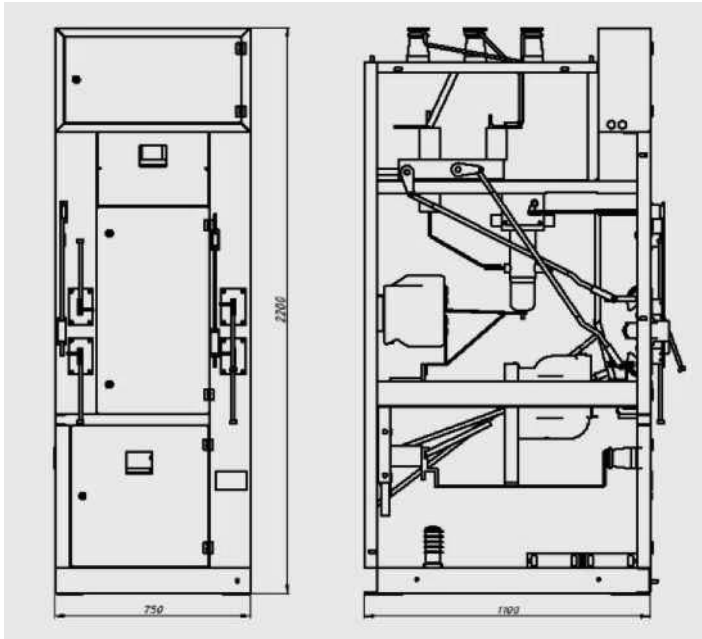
Внешний вид и габаритные размеры камер КСО-205К.
